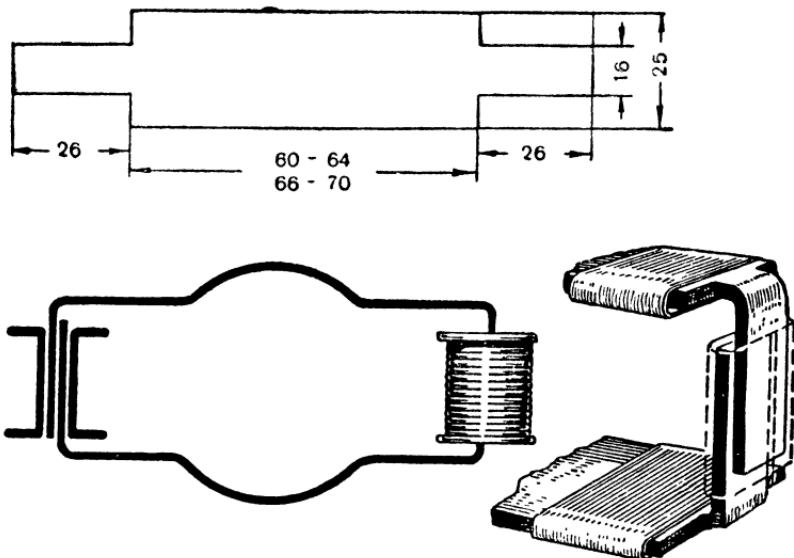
Устройство статора № 4 (рис. 18) и заготовка скобы.
